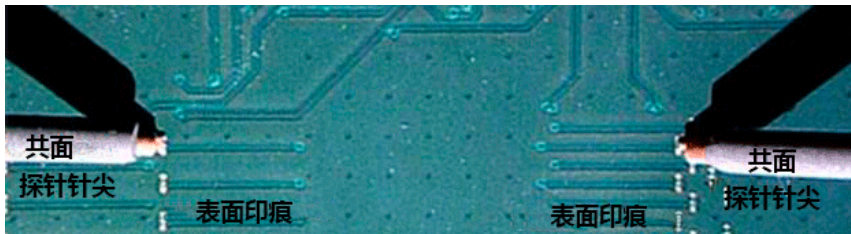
以封装互联为特色的英特尔 PCB 研究原型机。
